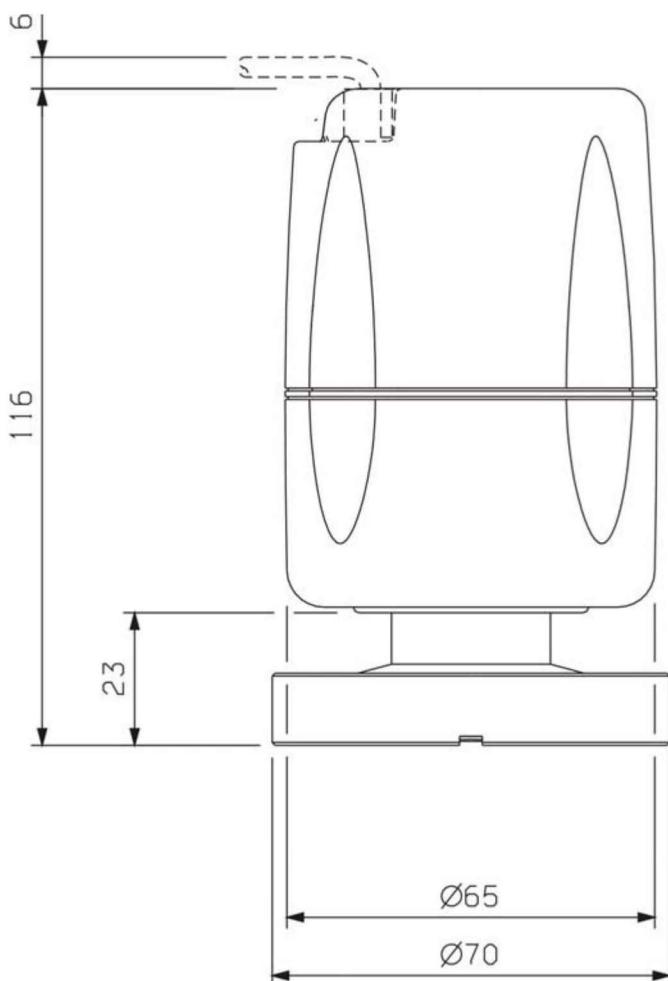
Dimensiunile (mm) WRG-S-DN40CF
